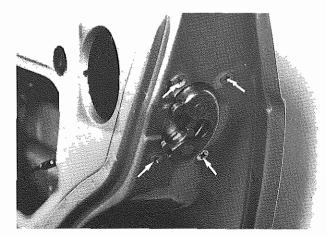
Viti fissaggio serratura Lock fixing screws
